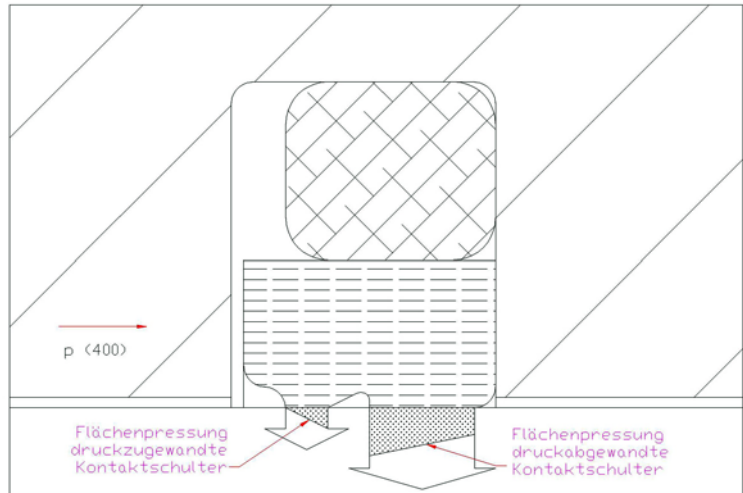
Dichtelement im druckbeaufschlagten Zustand
